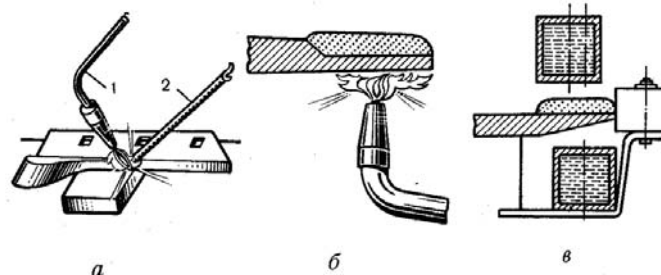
Способы нагрева лезвия плужного лемеха при наплавке твердого сплава: а — прямой нагрев прутка из твердого сплава «Сормайт-1» газовой горелкой; б — нижний нагрев лезвия с насыпной шихтой; в — нагрев токами высокой частоты; 1 — горелка; 2 — пруток из твердого сплава
